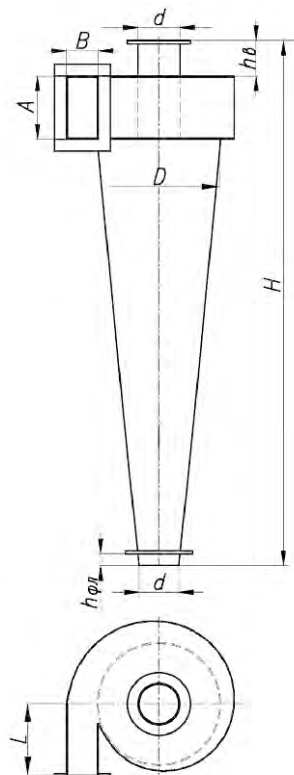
Габаритные и присоединительные размеры СДК-ЦН-33.
